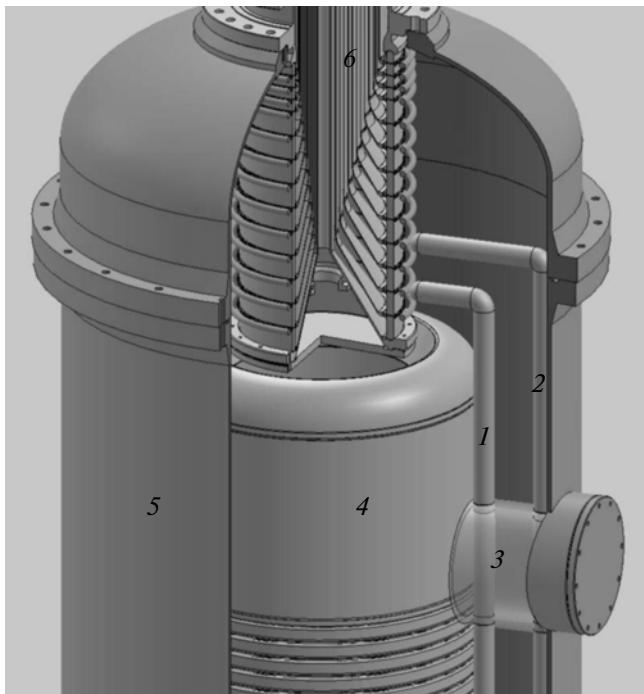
Приспособление для одиночного и последовательного подключения зазоров. 1 – штанга с высоким потенциалом; 2 – земляная штанга; 3 – изолятор; 4 – высоковольтный электрод выпрямителя; 5 – бак выпрямителя; 6 – газовая часть проходного изолятора.
